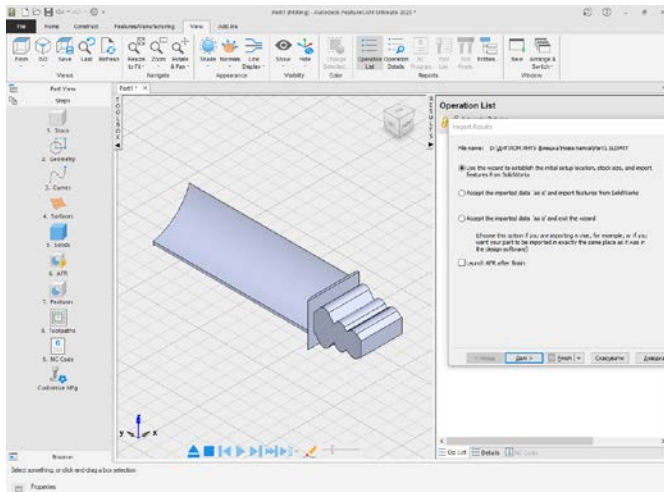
Розташування деталі (лопатка газотурбінного двигуна)
